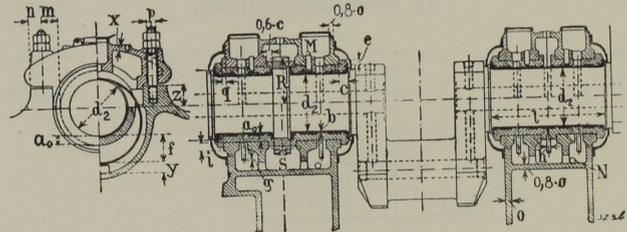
Lagerung der Kurbelwelle für Dieselmotoren.
